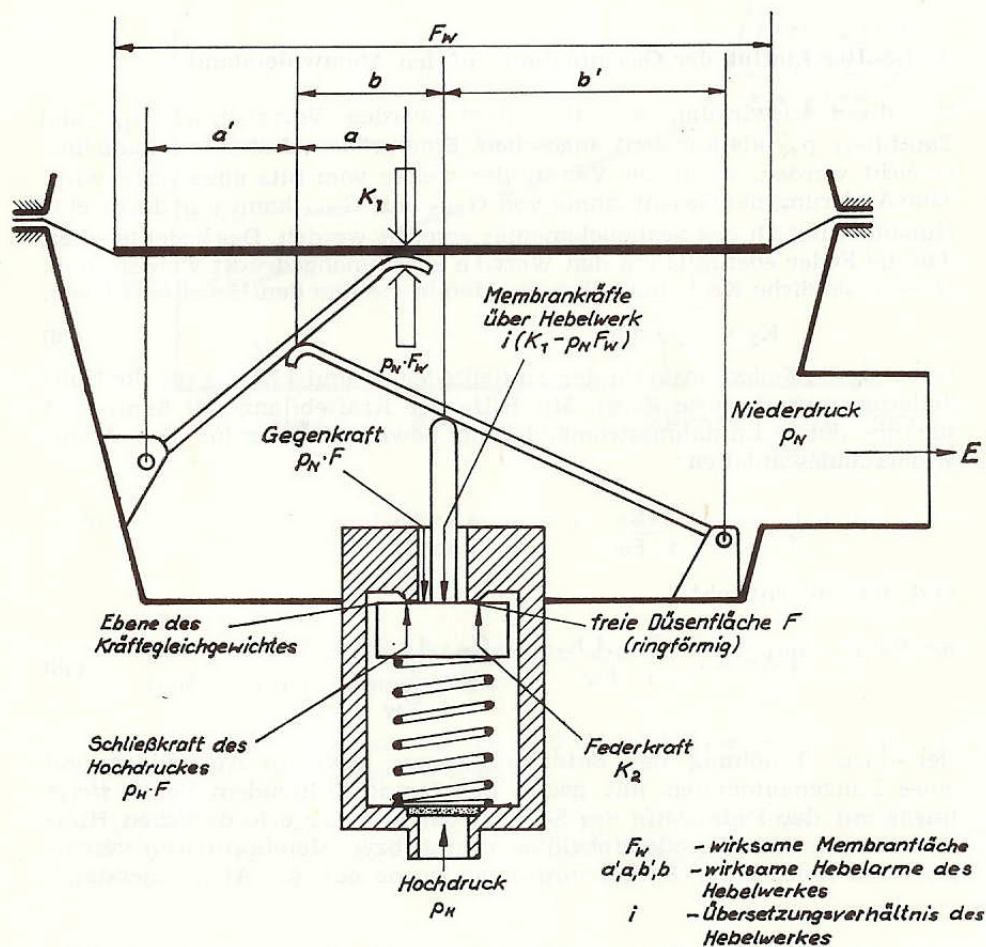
Funktionsschema eines einstufigen Lungenautomaten, dessen Ventil mit dem Druck dichtet, Hebelwerk zweifach ausgelegt
